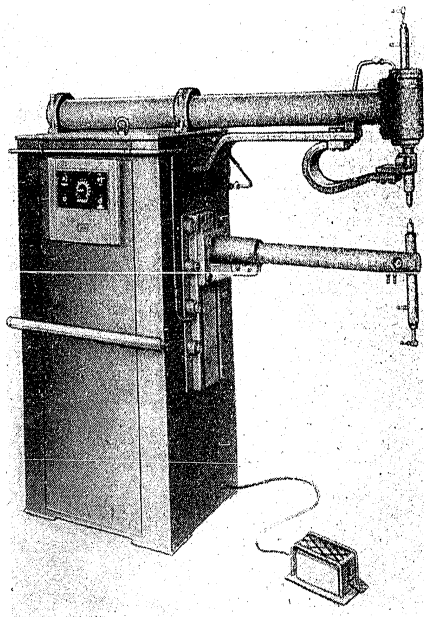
Elektrische Punktschweißmaschine (Ansicht)
